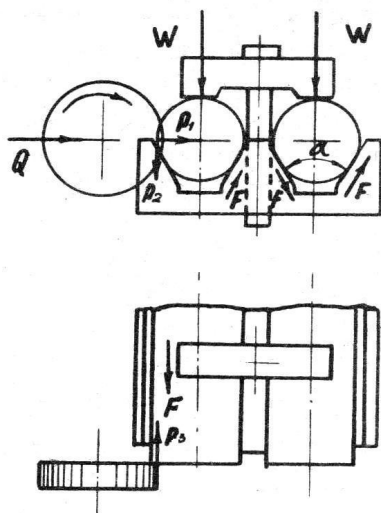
Схема установки, базування та закріплення заготовки в призмах з прихватами
